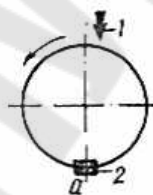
Расположение прихваток при сборке под двустороннюю автоматическую сварку под флюсом:
